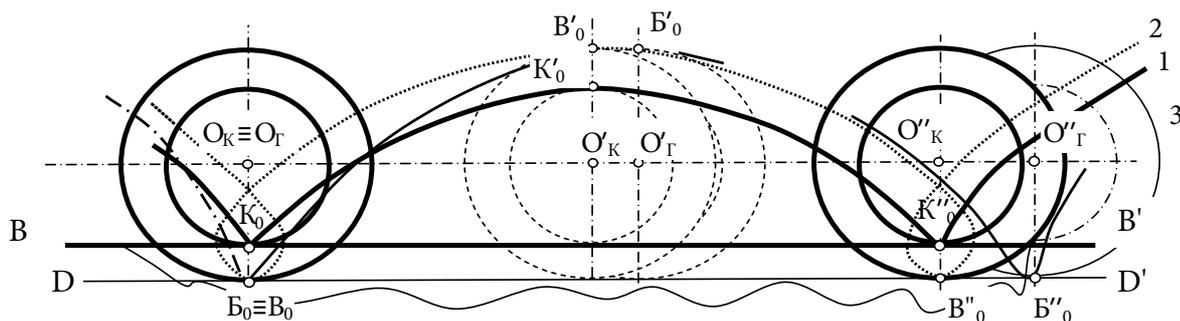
Траектории движения точек контактов поверхностей катания стандартной и новой конструкций колес с рельсами.
